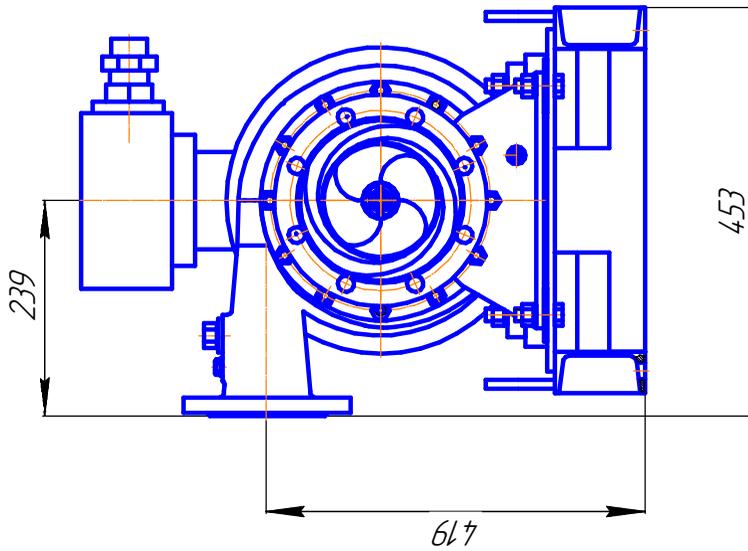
Габаритные размеры насосной установки для насосов с вертикальным и горизонтальным расположением напорного патрубка.
